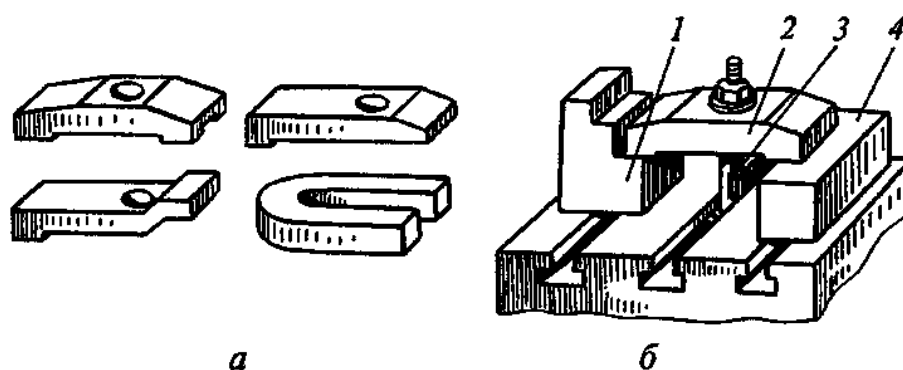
Прихваты и подставка: а - прихваты для крепления детали непосредственно на столе станка; б - прихват, опирающийся на подставку: 1 - подставка; 2 - прихват; 3 – болт; 4 – заготовка
